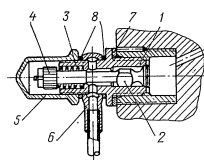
Пусковой клапан (разрез). 1—корпус, 2—клапан, 3—пружина, 4—гайка, 5—кольцо, 6—поворотный штуцер, 7—прокладка, 8—пружина.
